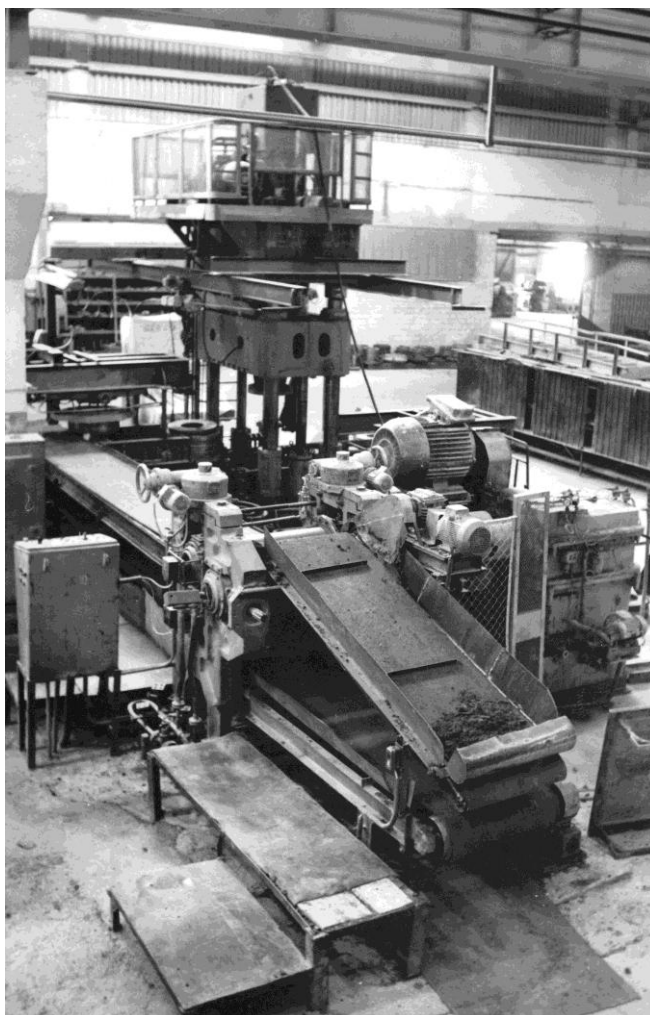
Поточно-механизированная линия для производства цилиндрических заготовок абразивных кругов
